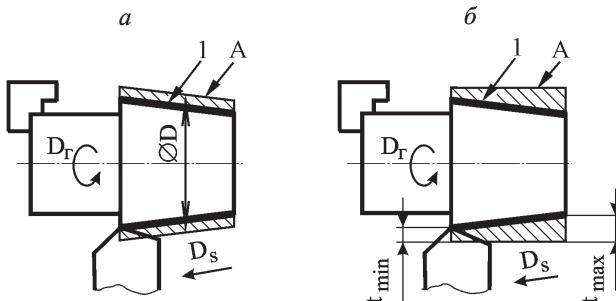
Схемы обтачивания конической поверхности 1 при конической (а) и цилиндрической (б) форме обрабатываемой поверхности А
